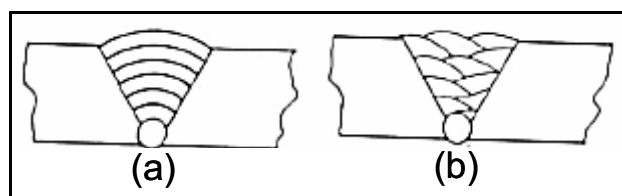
As técnicas de soldagem de (a) trançar e (b) filetar.
